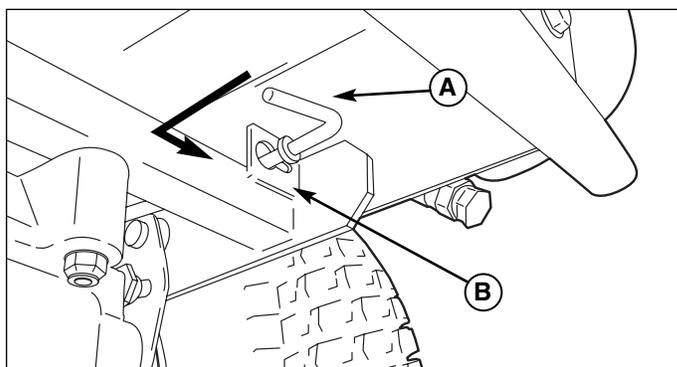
Composants de dégagement des rouleaux (de chaque côté)
